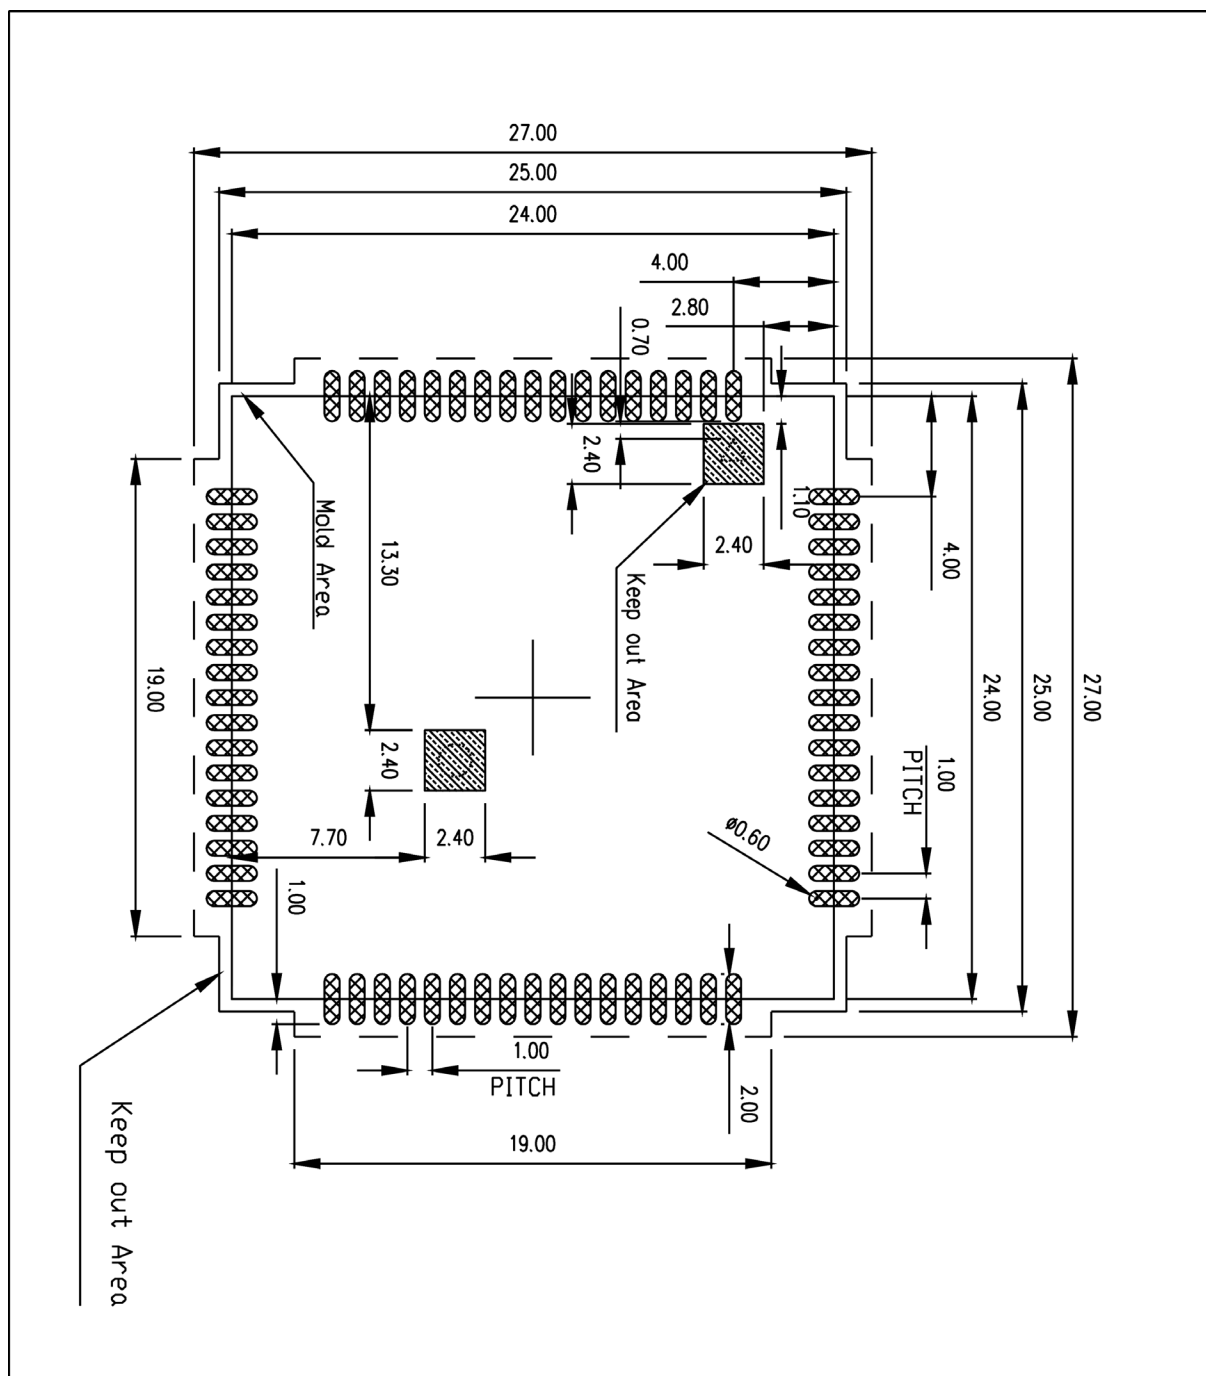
推荐 PCB 封装尺寸 (单位: 毫米)
